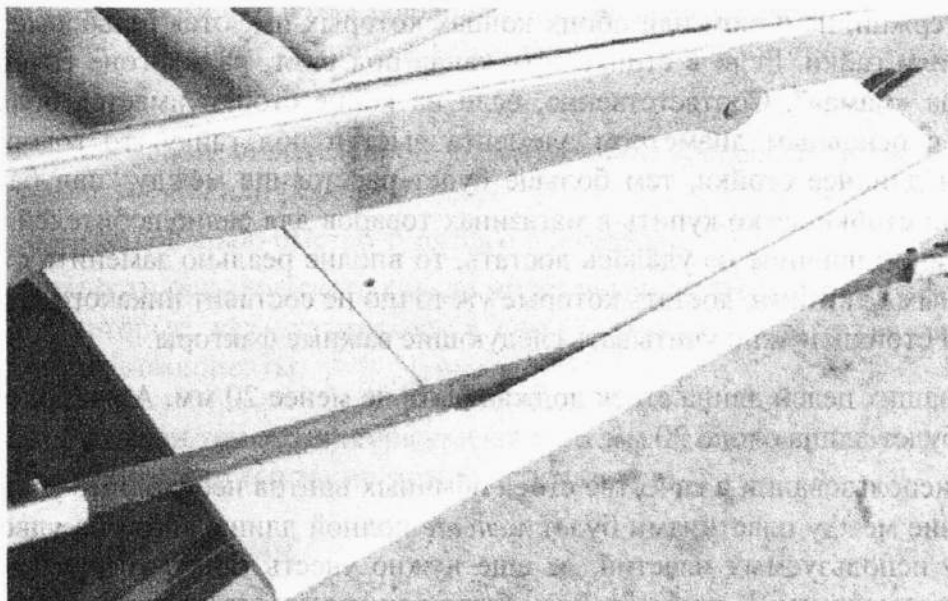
Разрезать заготовку на пластины можно при помощи ножовки
